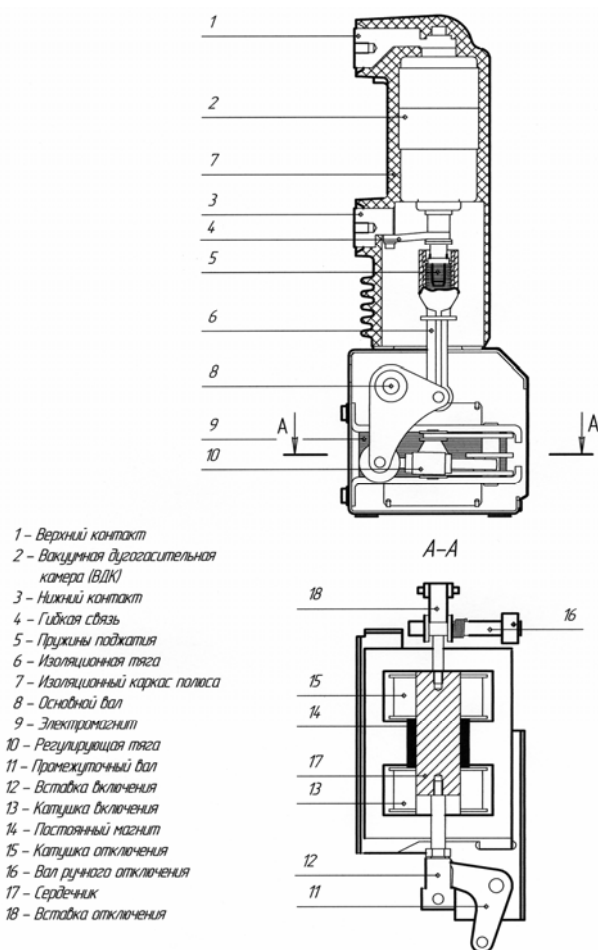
Вакуумный выключатель серии ВР0, ВР1, конструкция
